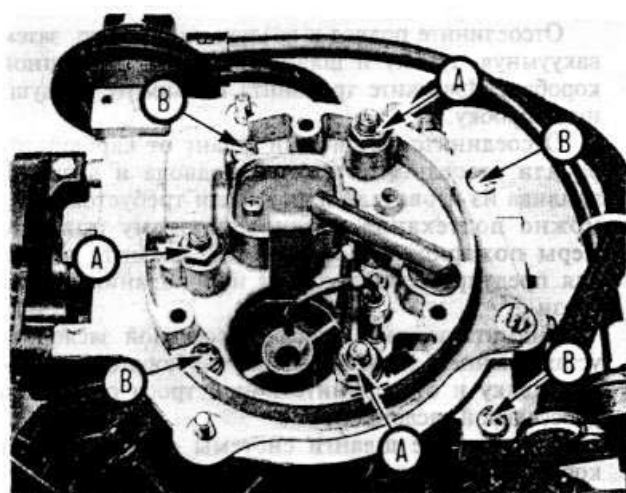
Гайки карбюратора (А) и винты верхней крышки (В)
